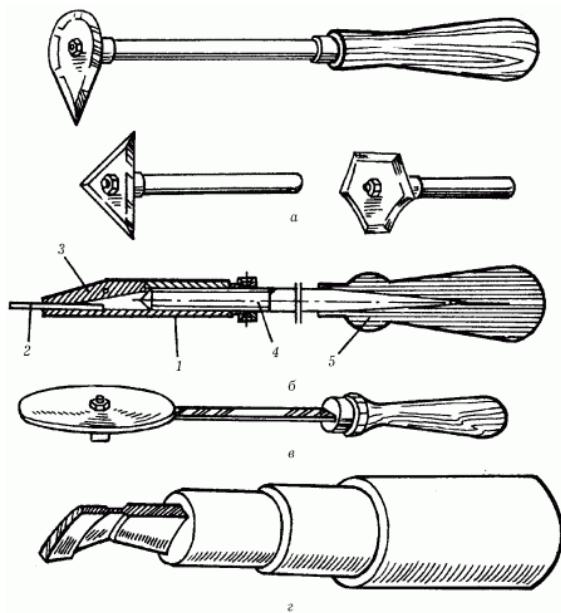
Виды шаберов: а – фасонные; б – вставной: 1 – корпус шабера; 2 – сменная режущая пластинка; 3 – зажимной кулачок; 4 – винт; 5 – рукоятка; в – дисковый; г – с радиусной заточкой
